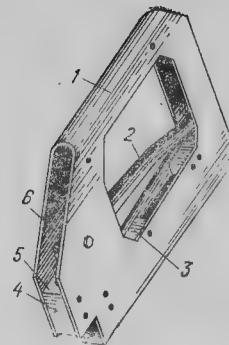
1 — корпус; 2 — рычаг спусковой; 3 — механизм ударный; 4 — нож (пуансон) неподвижный; 5 — нож (матрица) подвижный; 6 — пружина рычага возвратная
